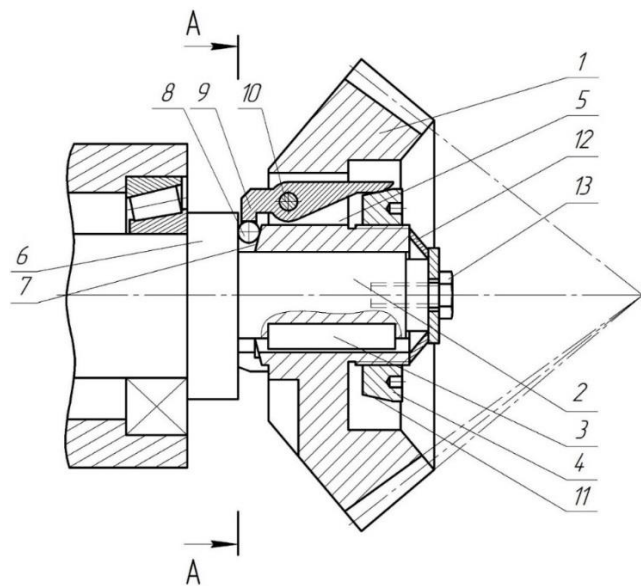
Пристрій для регулювання зачеплення конічних шестерень
